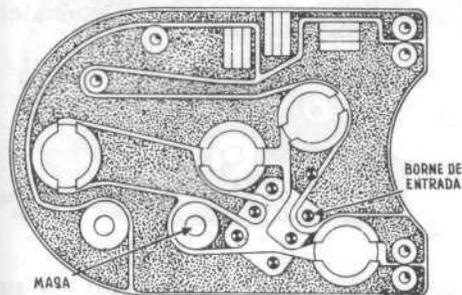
Sección izquierda del circuito impreso. Prueba del indicador de nivel de combustible.
